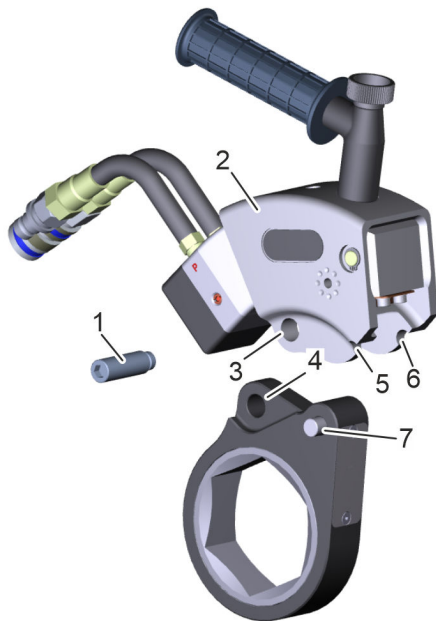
collegamento della testa a cricchetto al gruppo di azionamento
